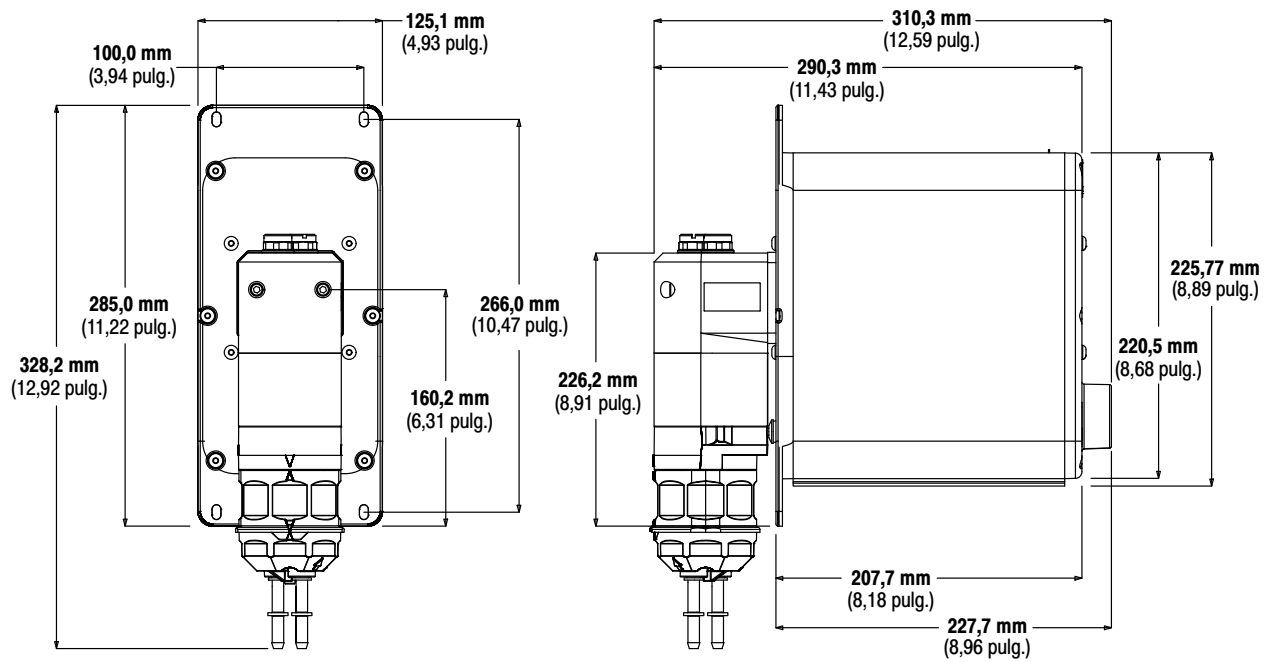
Dimensiones del módulo de bomba Encore HD+, XD
